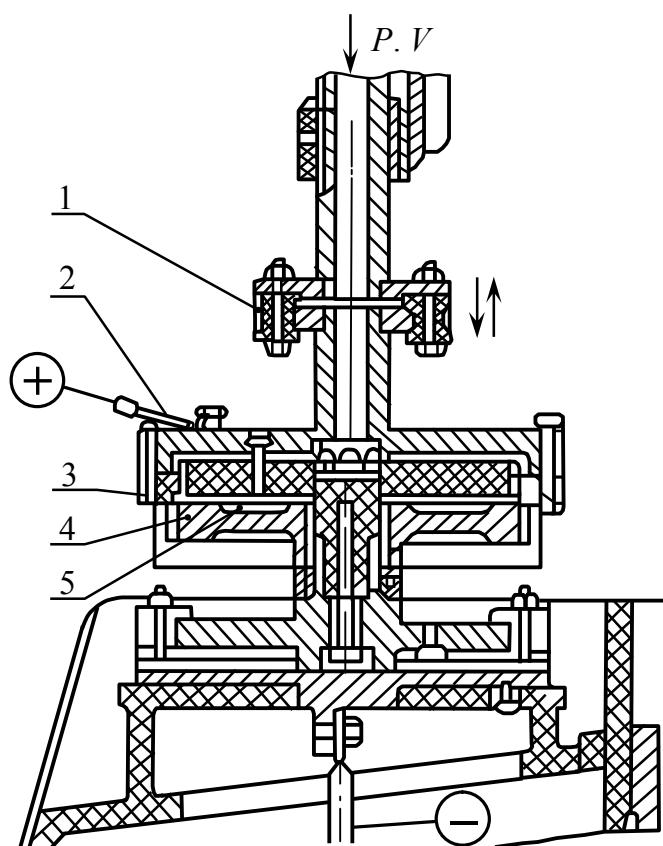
Схема одностороннего скругления острых кромок цилиндрического зубчатого колеса:
